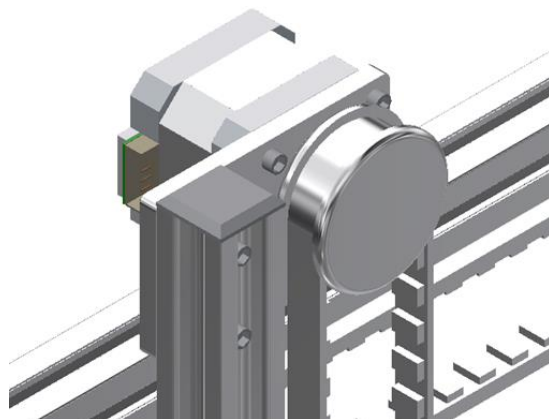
Acoplamiento de la correa en el motor a pasos, (Fuente, autor).
